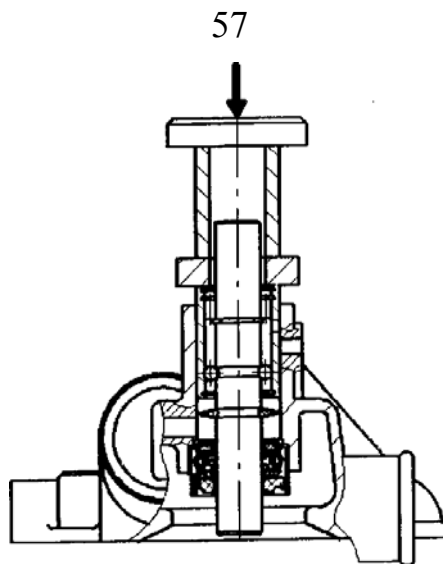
Запрессовка подшипника с валиком водяного насоса в корпус
